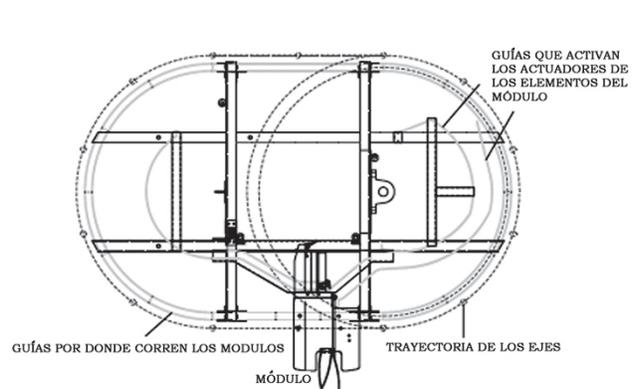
Vista esquemática lateral de las guías del módulo y de los actuadores.
